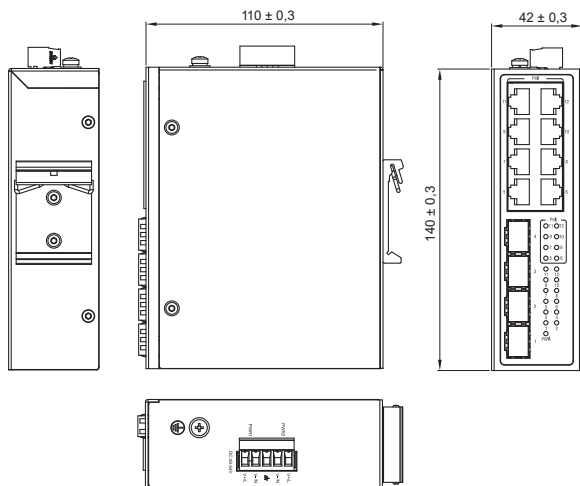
Габаритные размеры коммутатора ISU-450-4GX8GEPOE0000
